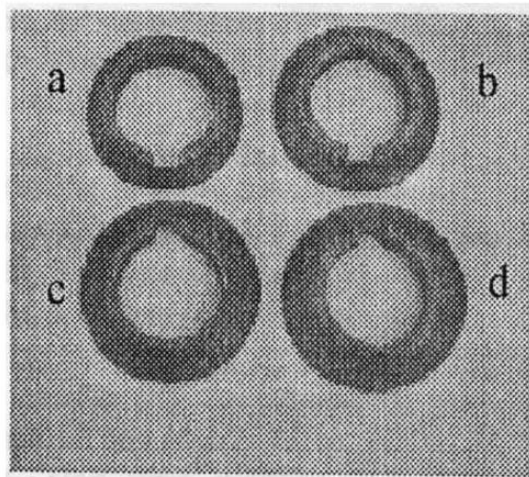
Anillos de presión (steamlocks) de extrusor Insta Pro 600 JR.
